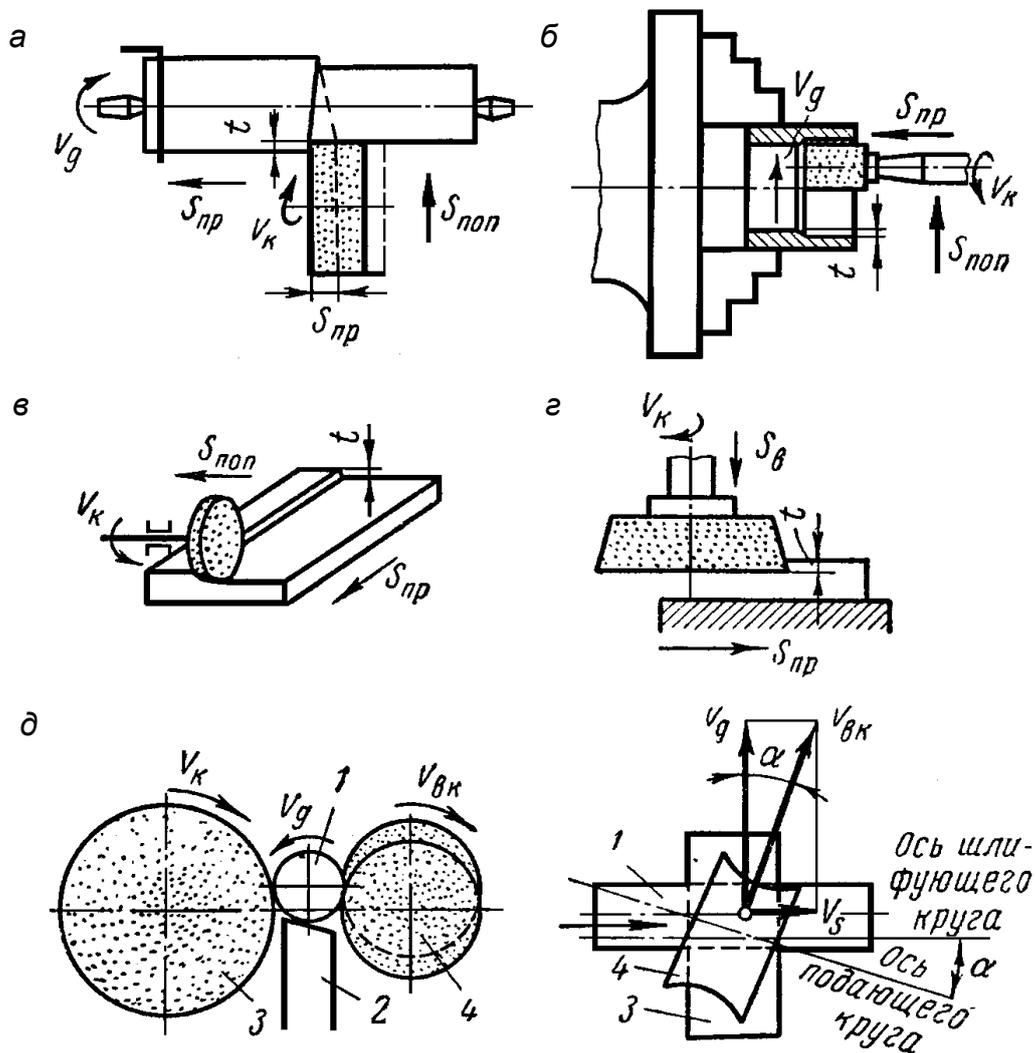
Основные виды шлифования: а – наружное круглое; б – внутренне круглое; в – плоское периферией круга; г – плоское торцом круга; д – бесцентровое наружное; 1 – деталь; 2 – упор; 3 – шлифовальный круг; 4 – ведущий круг
